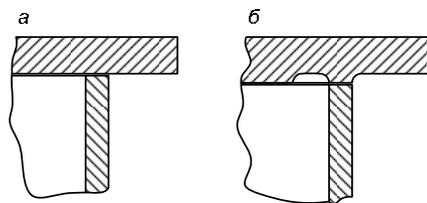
Конструкции соединения трубных решеток с корпусом:
